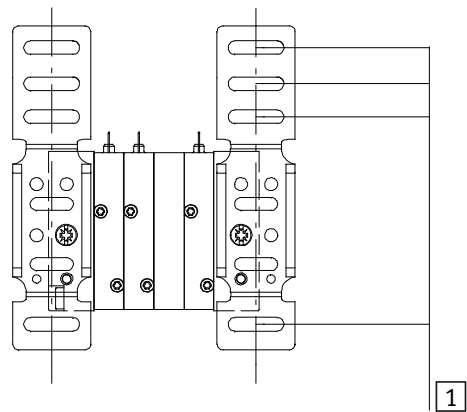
/2: Befestigungsbohrungen für die rückseitige Montage
